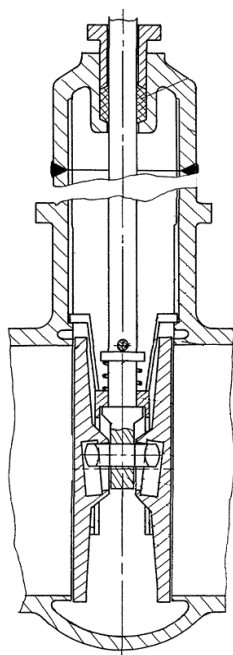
Общий вид задвижки двухдисковой конструкции Н. М. Калмыкова [18]
